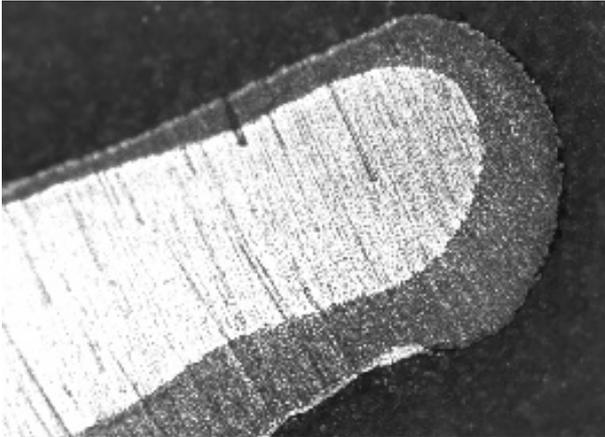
Makroschliff der Innenkante eines Fließbohrhohlrietes aus Stahlblech mit einem umschlossenen Blech einer Aluminiumlegierung
